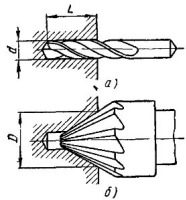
Сверление центрового отверстия сверлом (а) и зенковкой (б)
